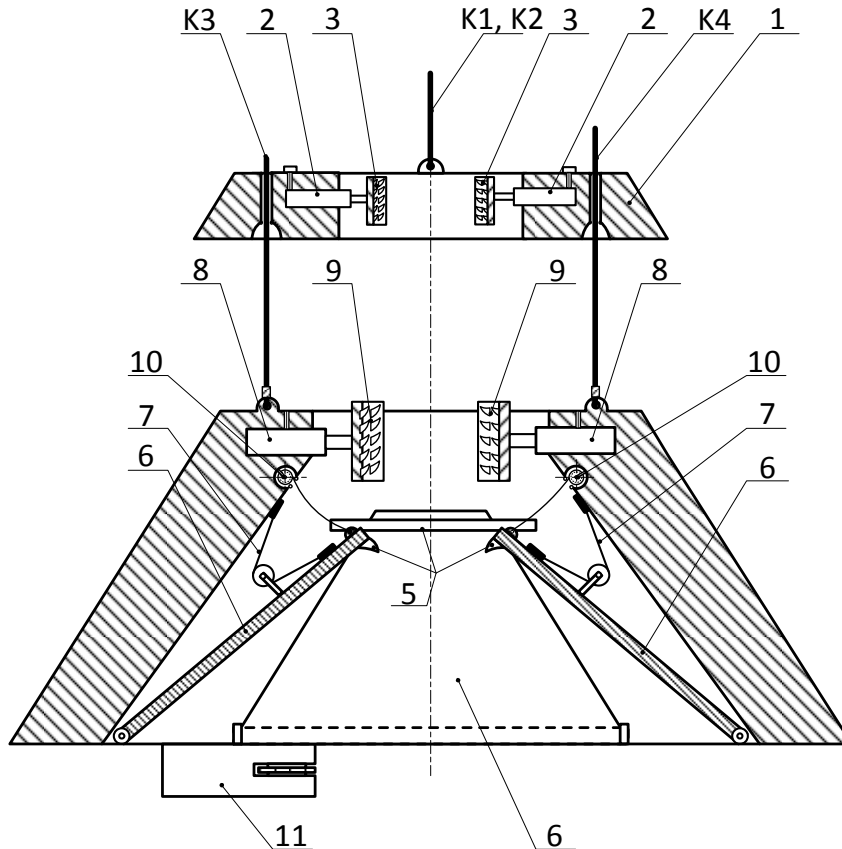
Общий вид разделяющегося грузозахватного механизма
